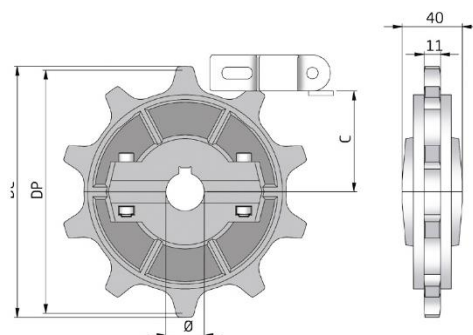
Planos de Piñón. Fuente: COBRA Cadenas
